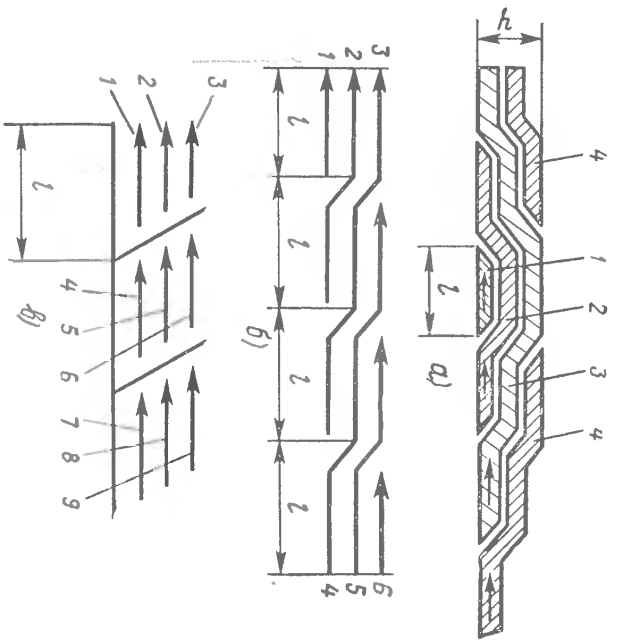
Способы сварки заготовок большой толщины:
